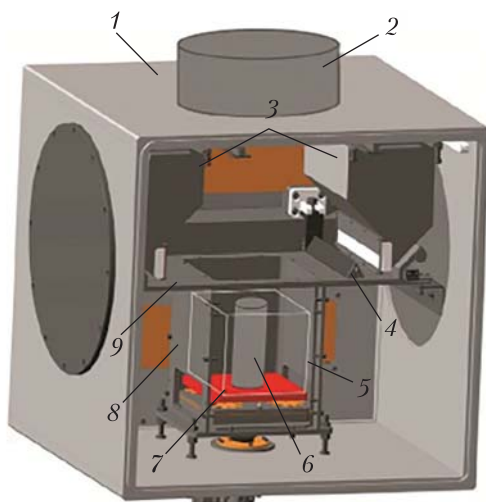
Установка для електронно-променевого 3D-друку: 1 — вакуумна камера; 2 — електронно-променева гармата; 3 — бункери; 4 — рейка; 5 — спечений порошок; 6 — виріб; 7 — платформа; 8 — шахта; 9 — стіл
